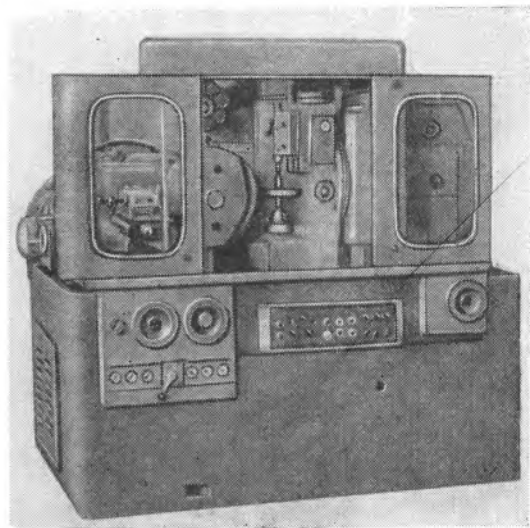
Зубошлифовальный полуавтомат 5B832 для обработки цилиндрических зубчатых колес
